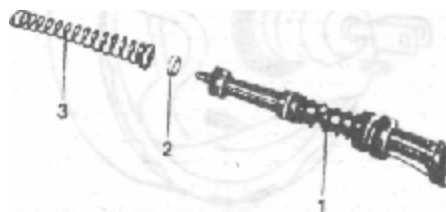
Поршень главного тормозного цилиндра в сборе
